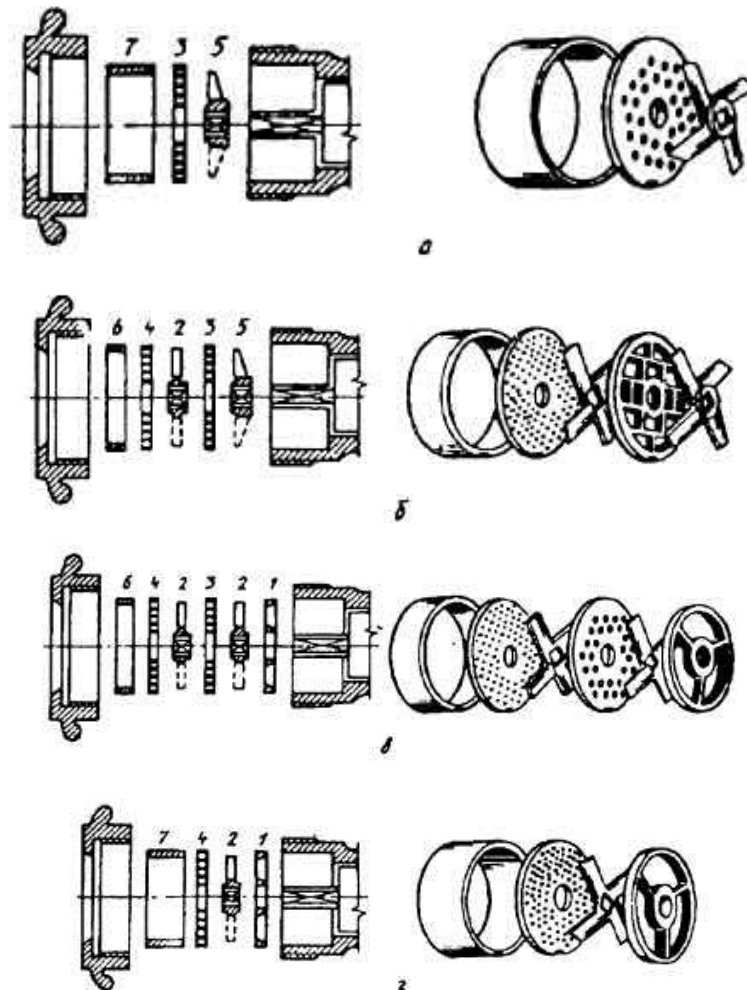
Схема зборки подрібнювальних механізмів вовчка
